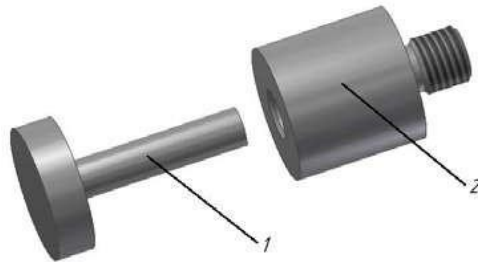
Оснастка для запрессовки изолятора в кабельный соединитель (ЖНКЮ.296361.018)
